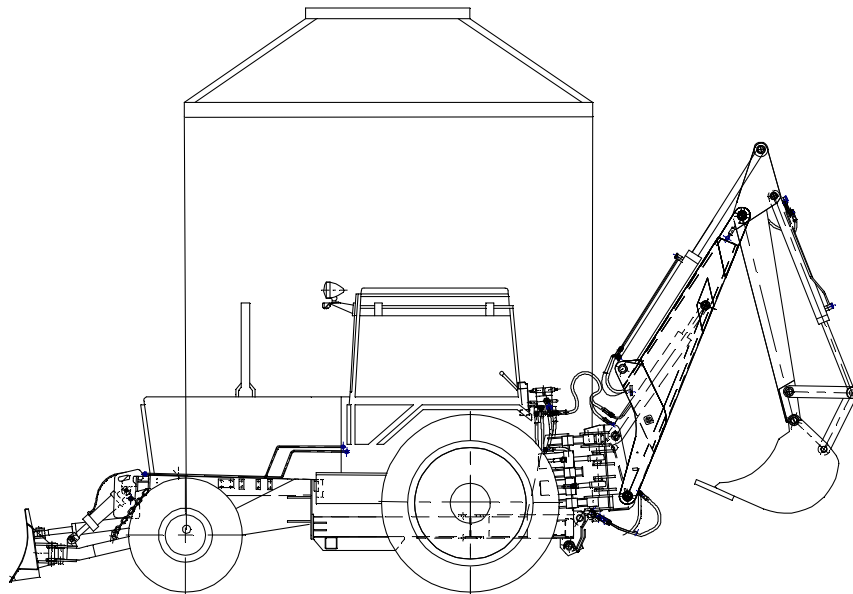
Схема строповки экскаватора-бульдозера 702ЕВ
